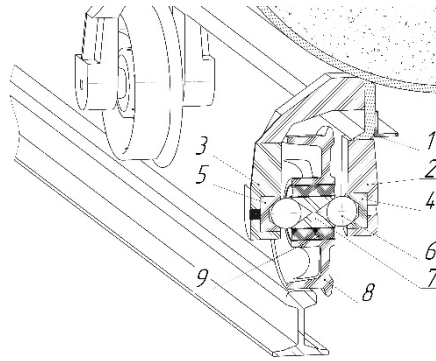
Принципова конструкція буксового вузла з додаткових ступенем рухливості колеса: 1 - рама; 2, 3 - стійки; 4, 5 - упорні втулки; 6 - куля; 7 - упорно-направляюча втулка; 8 - колесо; 9 – компенсуючий елемент
